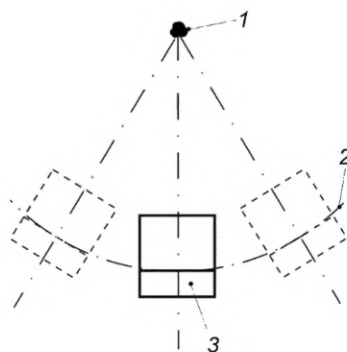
Пример прозвучивания сварного шва
